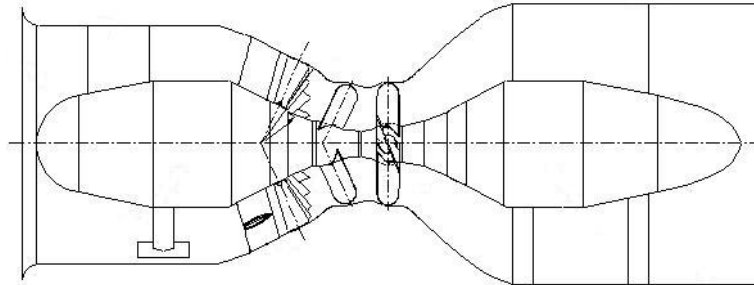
Сдвоенный прямоточный гидроагрегат
